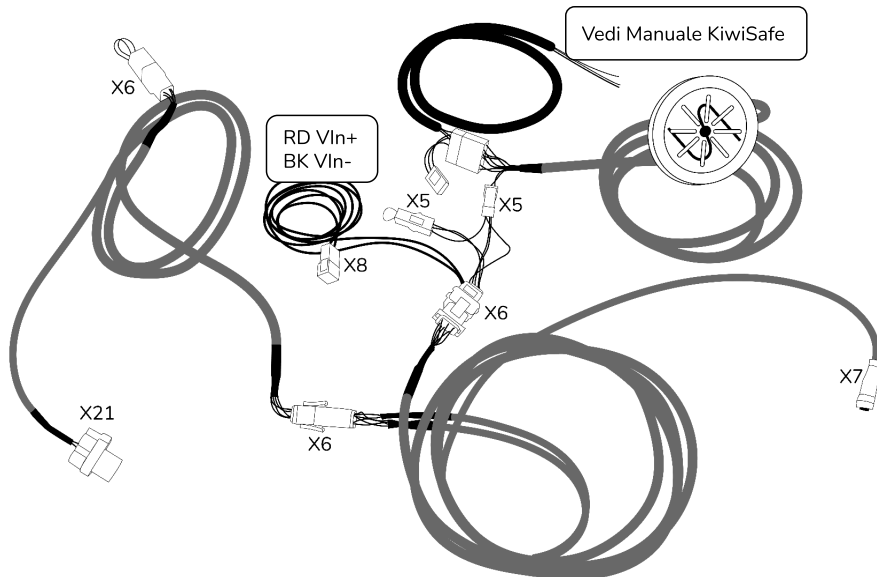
Collegamento KiwiSafe + KiwiEye + KiwiPad - Wi-Fi (C002702)
